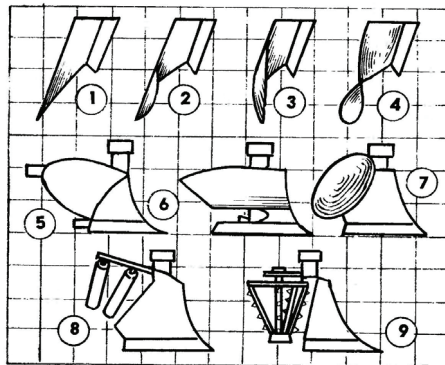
Конструкции корпусов отвальных плугов: 1 – цилиндрический; 2 – культурный; 3 – полувинтовой; 4 – винтовой; 5 – со сменной грудью; 6 – вырезной; 7 – дисковый; 8 – роликовый; 9 – с ротором
